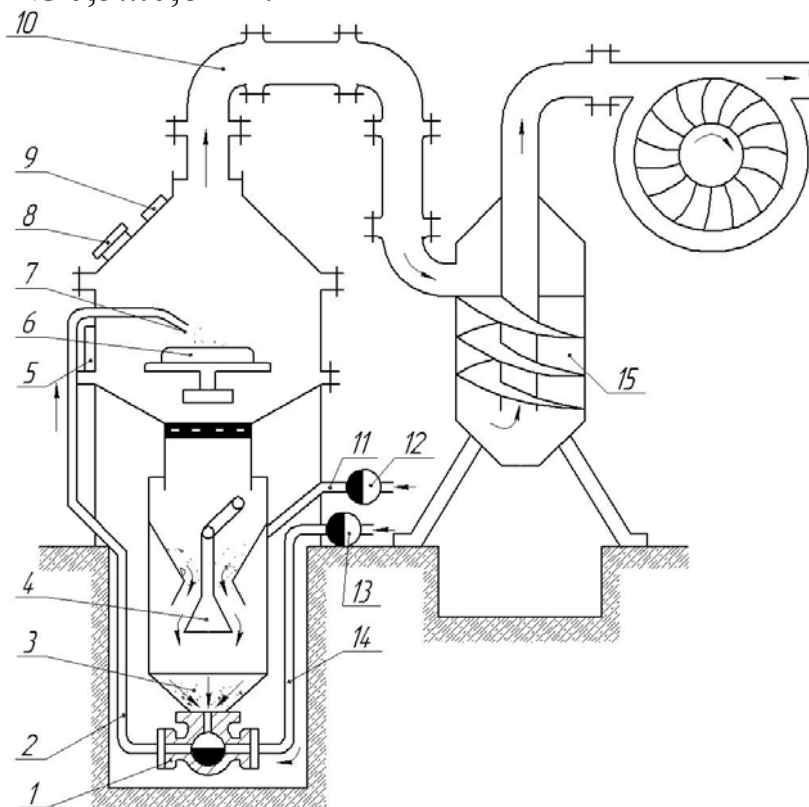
Установка для пневмомеханічного очищення деталей кісточковою крошкою:
